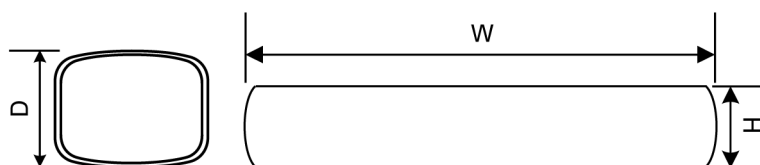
Skjematisk fremstilling, dimensjoner i millimeter
